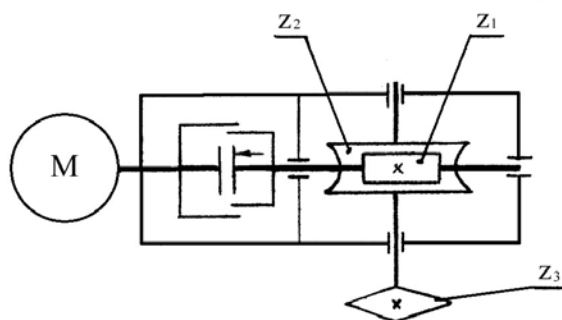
Кинематическая схема проектируемого червячного редуктора
